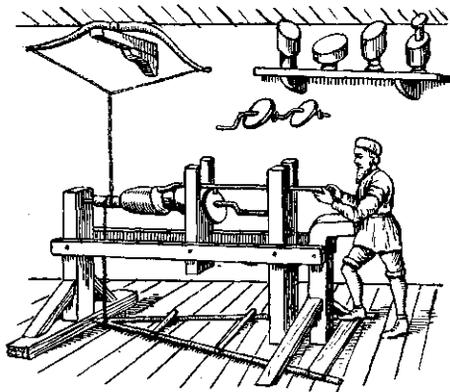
Токарно-овальерный станок Жака Бессона 1569 г. с ножным лучковым приводом.
